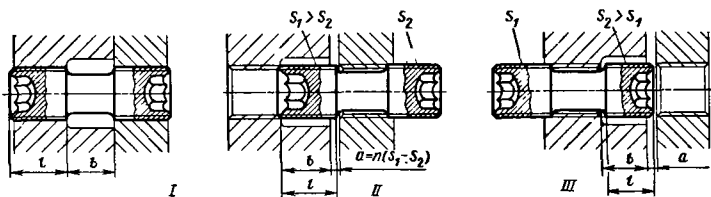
Соединение деталей болтом с дифференциальной резьбой: I и II — положения после и перед сборкой; III — вариант сборки
